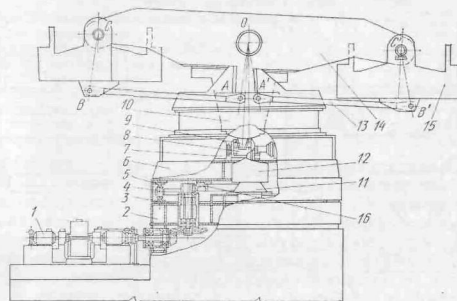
Поворотный сталеразливочный стэнд конструкции УЗТМ
